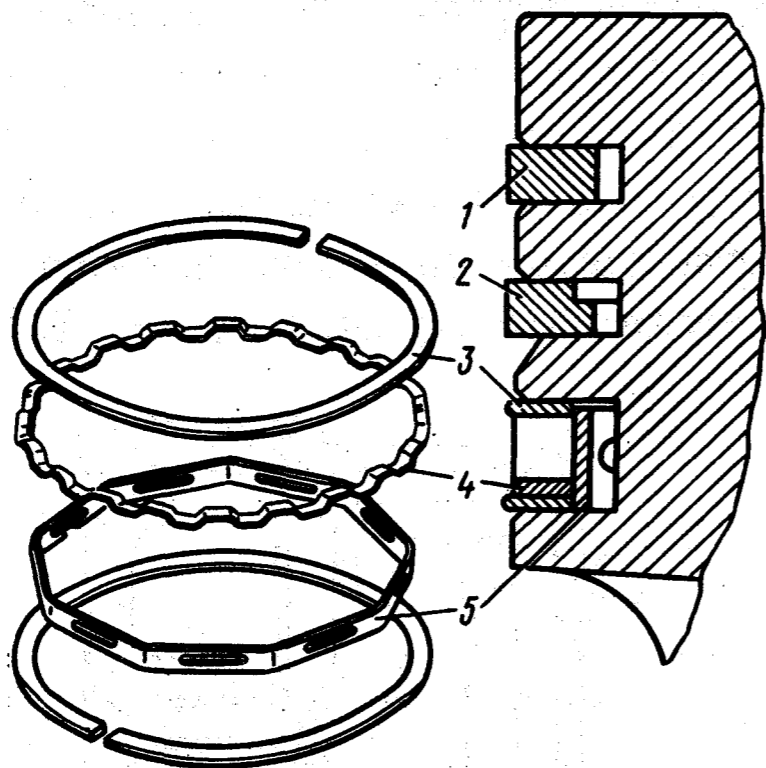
Установка поршневых колец на поршень: 1 — кольцо верхнее компрессионное; 2 — кольцо нижнее компрессионное; 3 — диск кольцевой; 4 — расширитель осевой; 5 — расширитель радиальный
